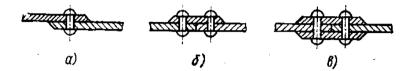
Виды заклепочных соединений: а – нахлесточное; б – стыковое с одной накладкой; в – стыковое с двумя накладками
